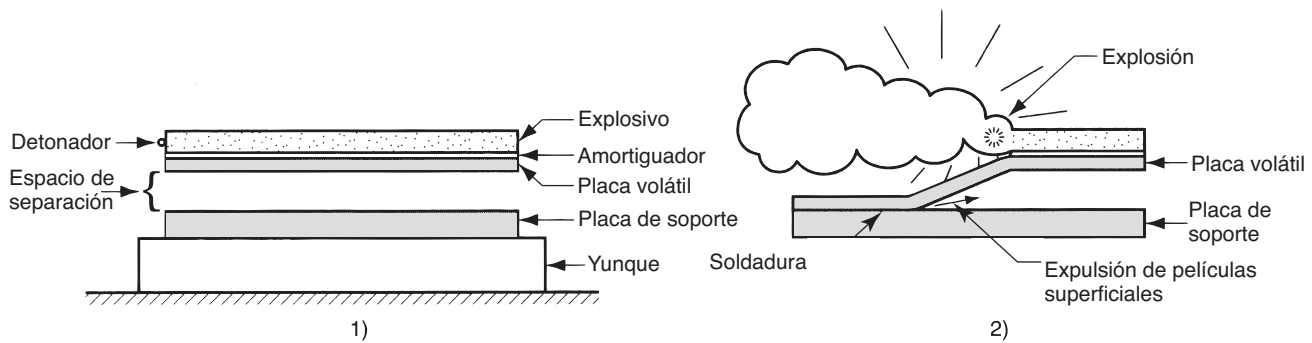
Soldadura explosiva (EXW): 1) disposición en la configuración paralela y 2) durante la detonación de la carga explosiva.
